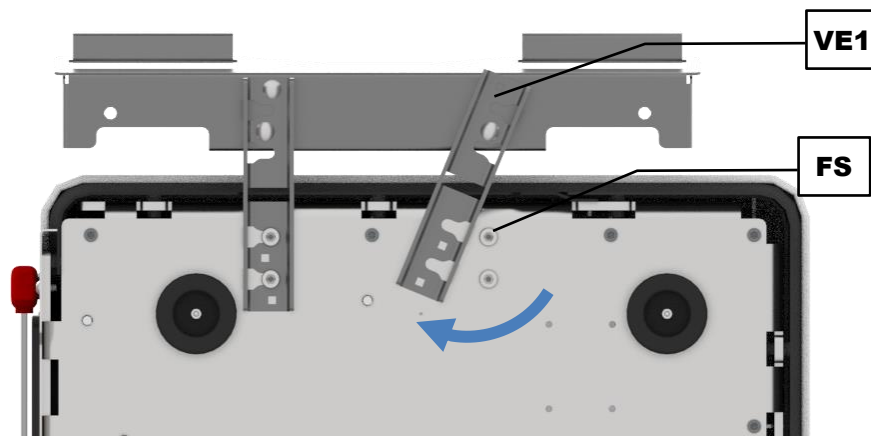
Приспособление для транспортировки — ослабление стопорного винта
